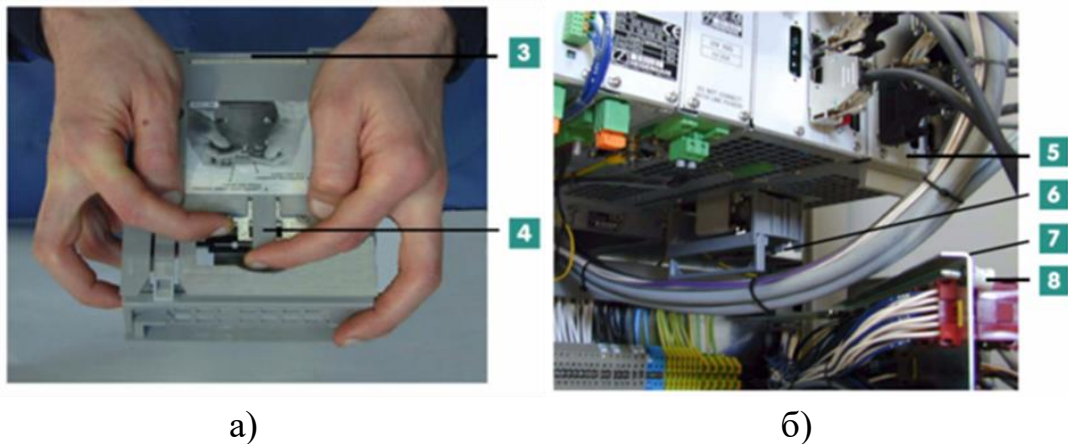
Основний контролер фрезерно-свердлильного верстата:
